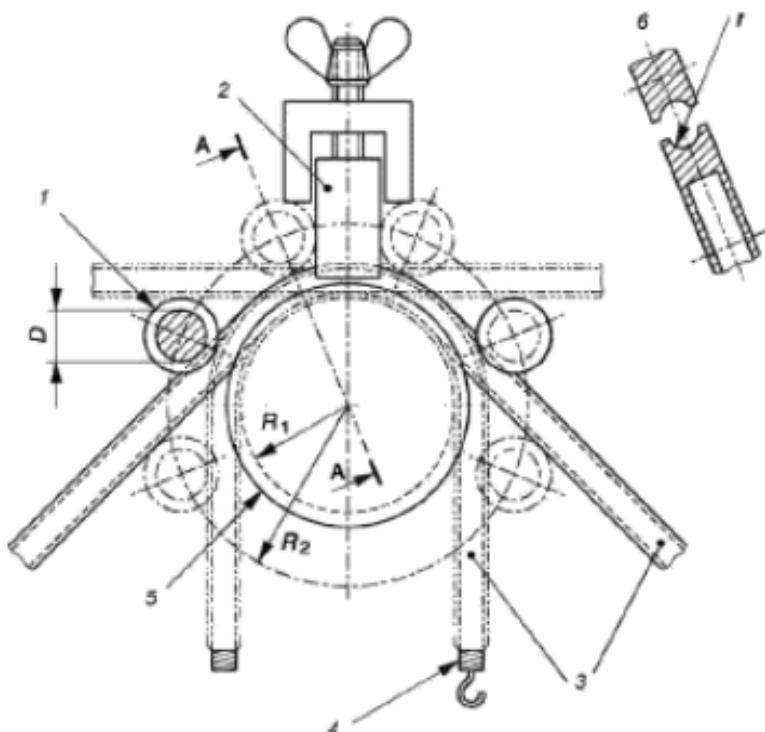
Установка для испытаний на изгиб металлических и композитных труб
